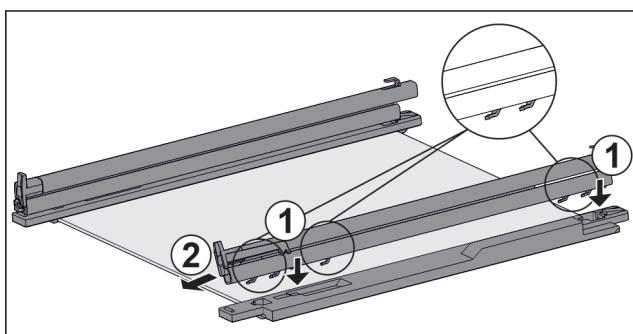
Скляна пластина з рейками та деталями для підтримки
